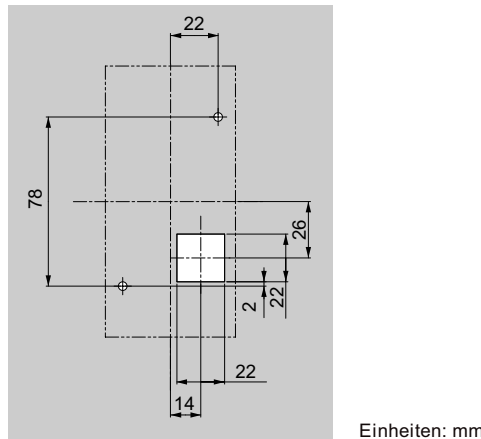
Abmessungen des Schrank-Ausschnittes (Externe/Frontmontage)
